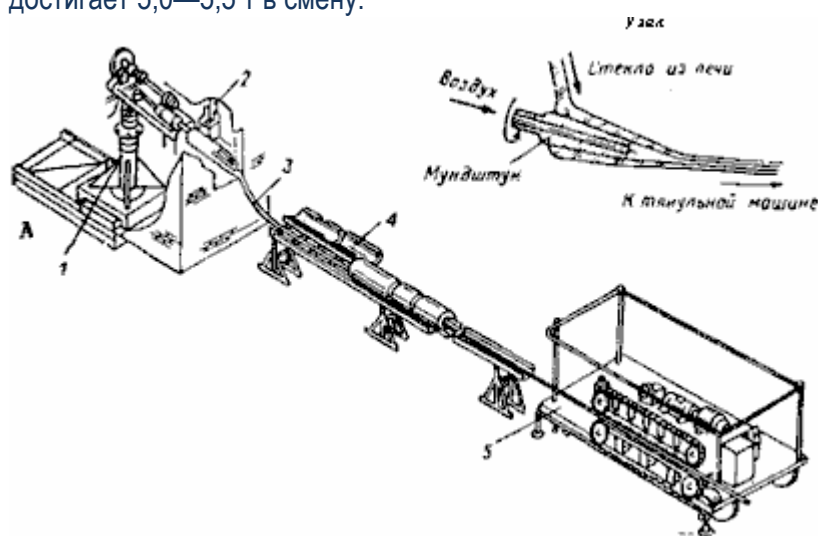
Установка для горизонтального вытягивания трубок: 1—мундштучная машина; 2 — шибер, регулирующий подачу стекла; 3— трубка; 4—отжигательный канал. 5—цепная тянущая машина.
